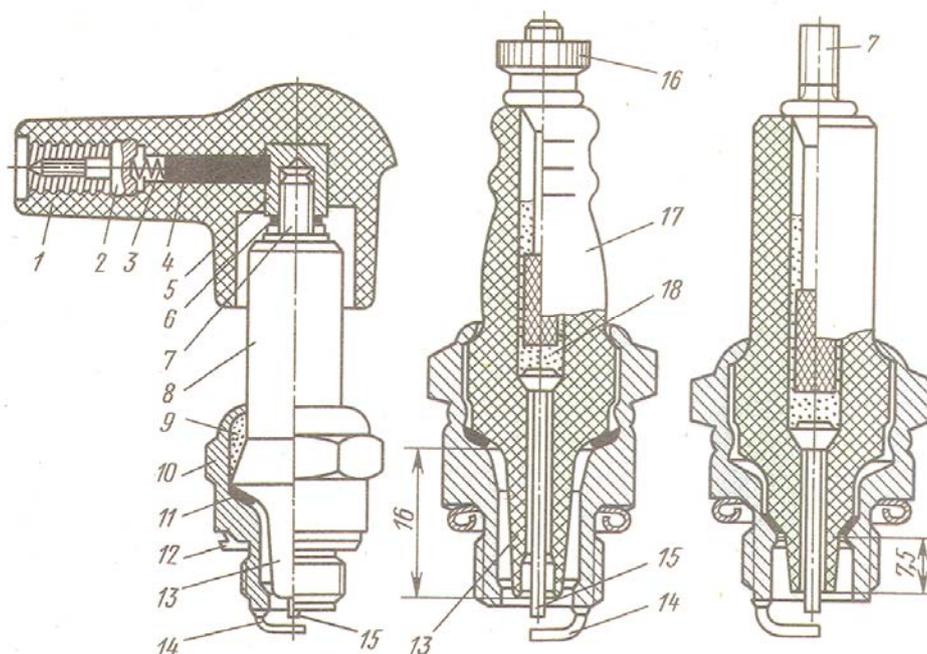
Свечи зажигания: а – устройство; б – горячая свеча; в – холодная свеча; 1 – корпус; 2 – вывод; 3 – контактная пружина; 4 – подавительный резистор; 5 – контакт; 6 – стопорная пружина; 7 – стержень центрального электрода; 8 – изолятор; 9 – уплотняющий порошок; 10 – корпус свечи; 11 – медная шайба; 12 – медно асбестовая шайба; 13 – тепловой конус; 14 – боковой электрод; 15 – центральный электрод; 16 – контактная гайка; 17 – контактная головка; 18 – токопроводящий стеклогерметик
